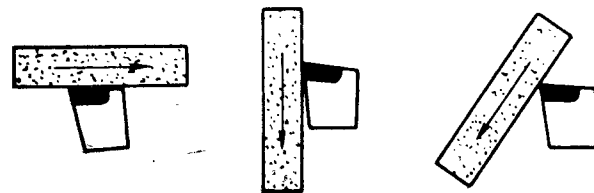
Правка и притупление твердосплавной режущей кромки ручным притиром
